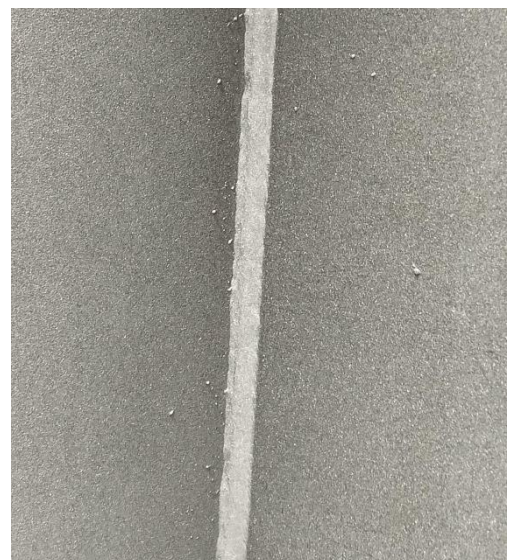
Cordón de soldadura preparado. 2025. Fuente: Elaboración propia.
